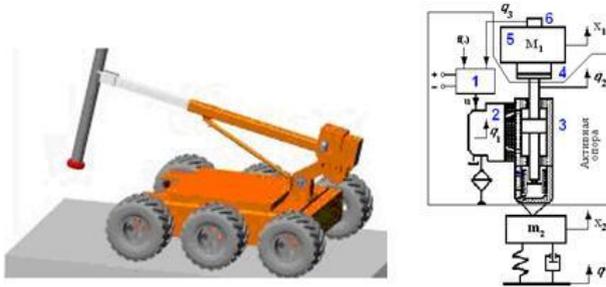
Компоновка мобильного робота и схема его активной опоры
